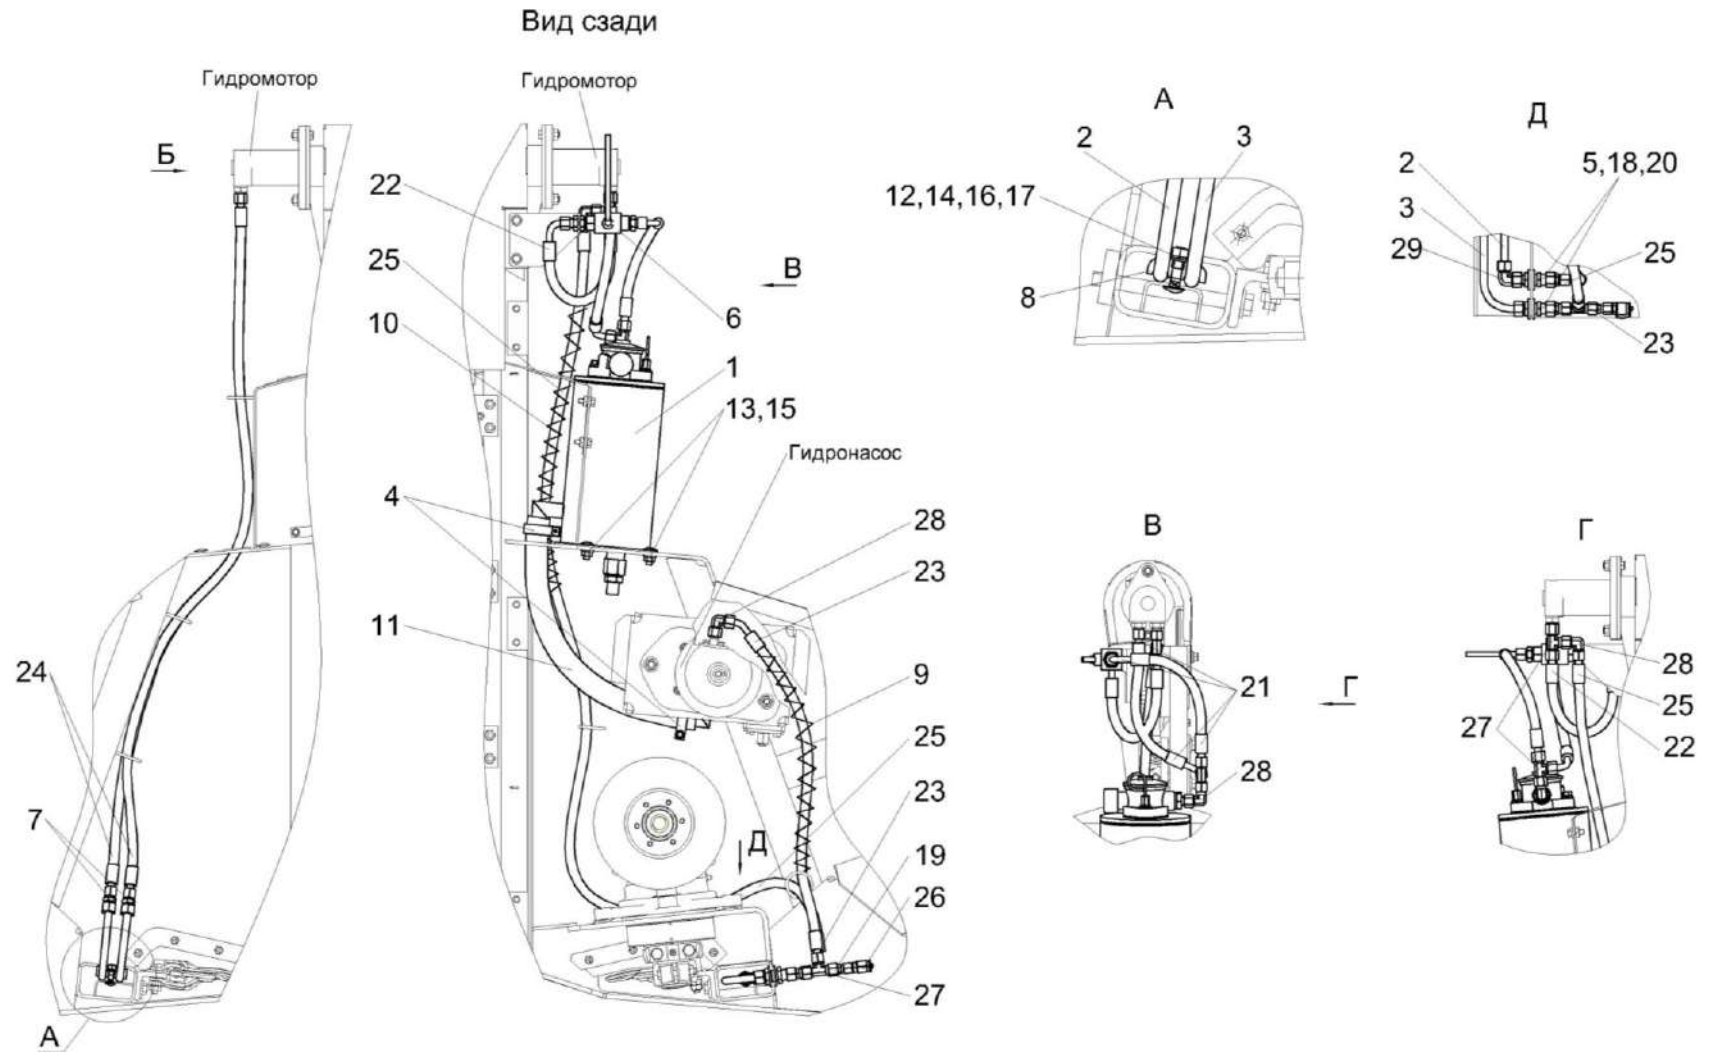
Гидросистема привода приспособления для уборки рапса КЗК 2542000А
